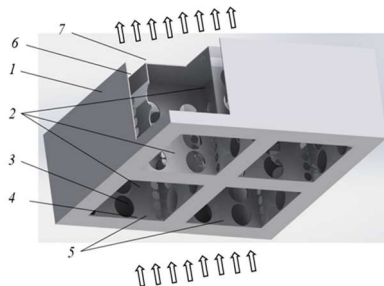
Блочный сепаратор (вид с разрезом): 1 – корпус; 2 – блоки; 3 – отверстия для выхода газа; 4 – боковые отверстия для выхода газа; 5 – вход в устройство; 6 – сепарационная зона; 7 – крышка съемная
